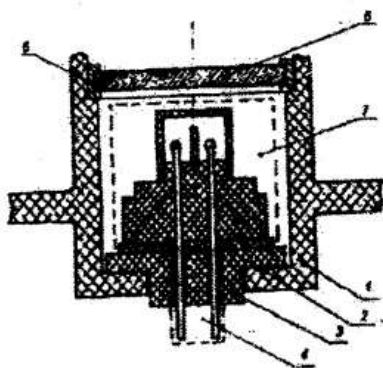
Конструкция датчика с двойным газодиффузионным фильтром : 1- корпус изделия; 2 – амортизатор; 3 – втулка; 4 – датчик в сборе; 5 – кассета; 6 – фильтрующий элемент; 7 – полость.
